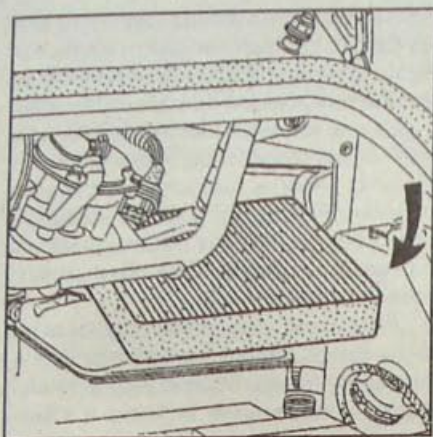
Установка фильтрующего элемента системы вентиляции
